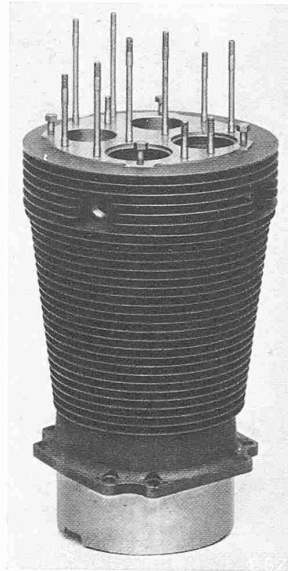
Aus dem Vollen herausgearbeiteter Zylinder.
